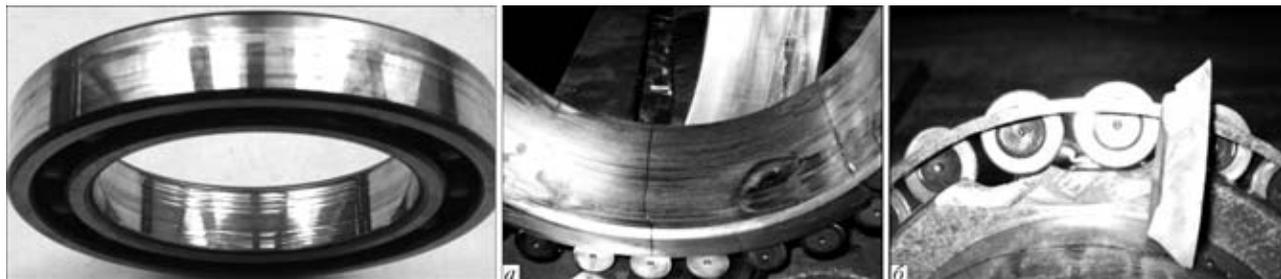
Следы проворачивания колец подшипника вследствие ослабления его посадки
